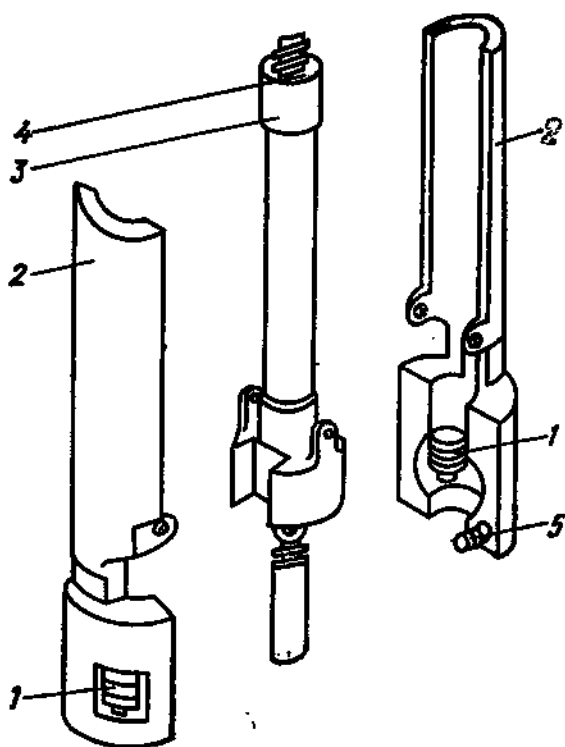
Узел ротора электродвигателя с роликовой гайкой:
